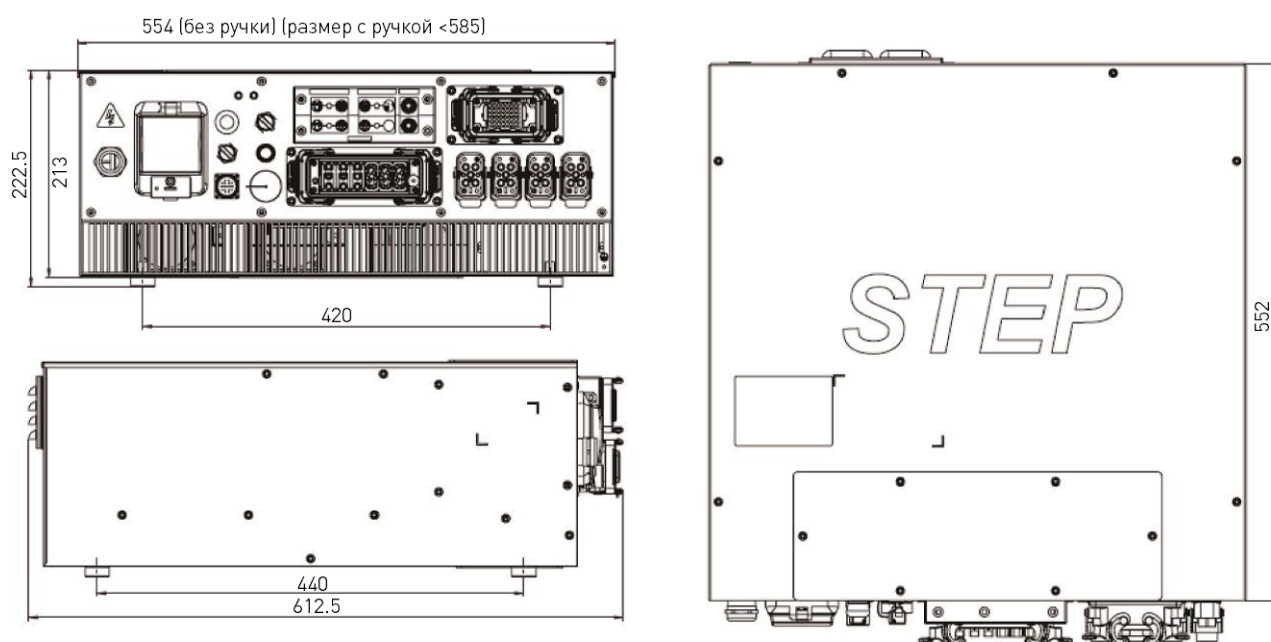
Размерный чертеж блока управления SRC4-L.
